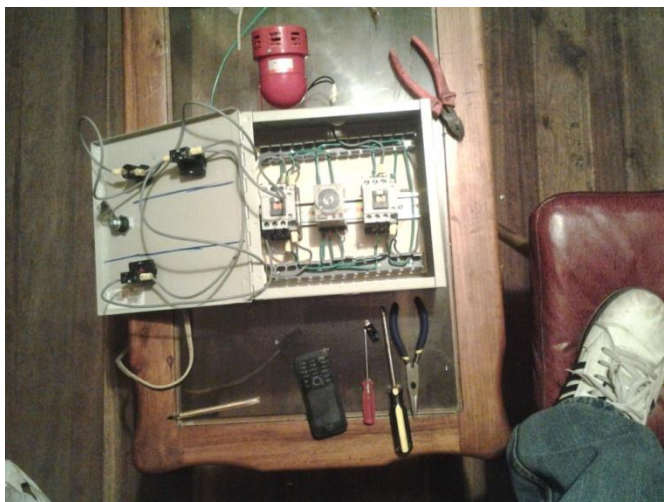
19. Ensamblaje con los elementos internos de la caja de control
